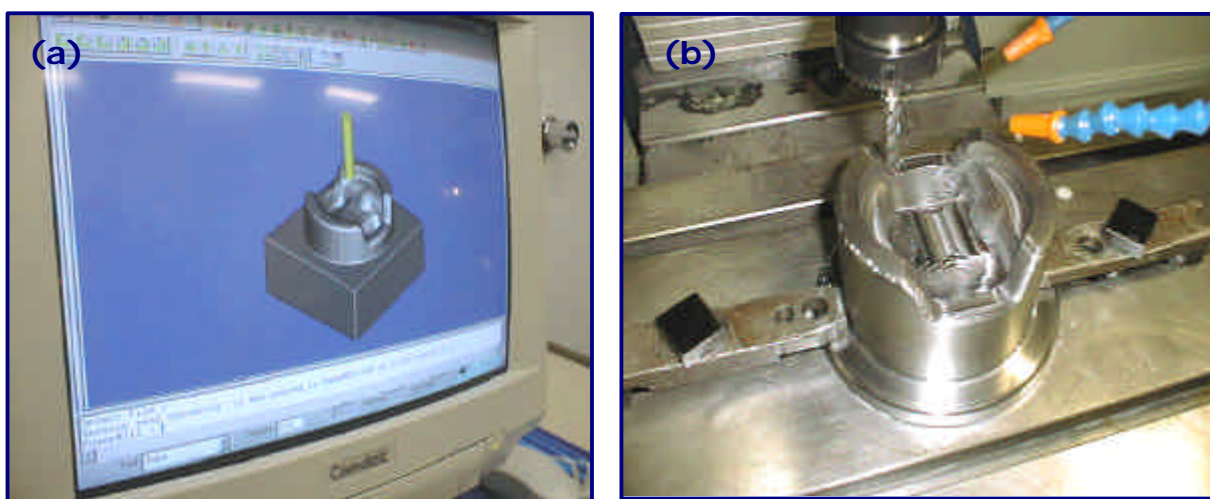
Detalhe da (a) simulação e (b) usinagem real da ferramenta
